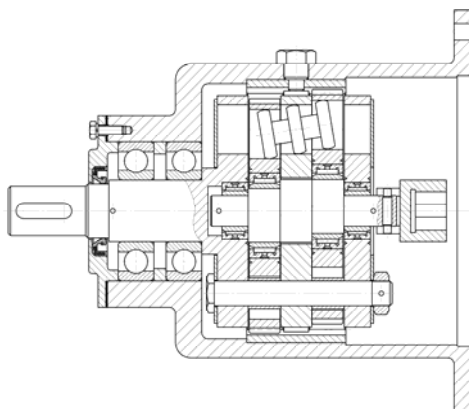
Конструкция передачи типа $K-H-V$ с качающимися роликами механизма снятия движения с сателлита
